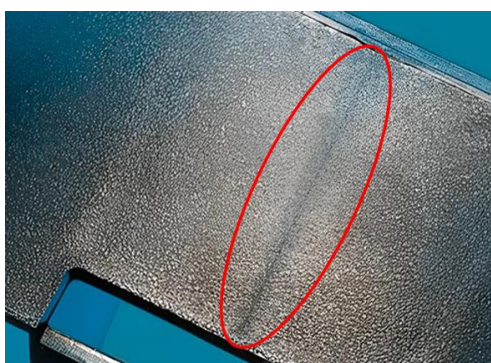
1 Línea de soldadura en una pieza fabricada por inyección [35]
